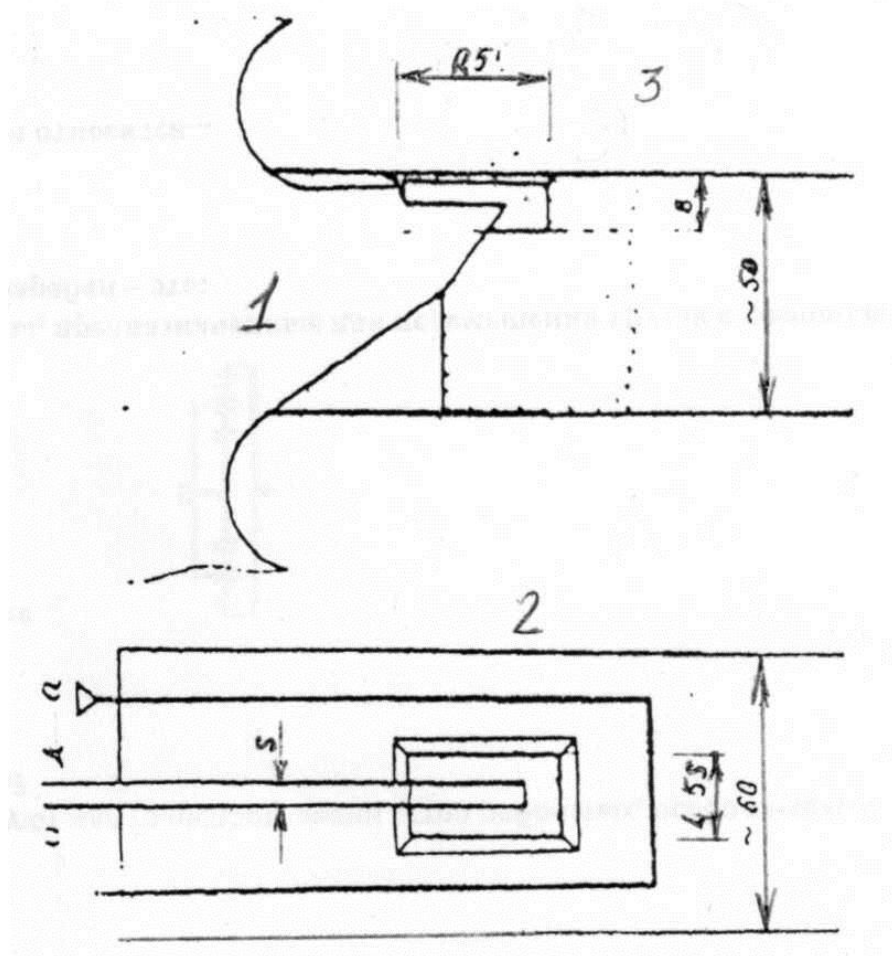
Схема расположения зуба пилы в приспособлении для наплавки: 1 – пила; 2 – приспособление; 3- наплавляемый материал
